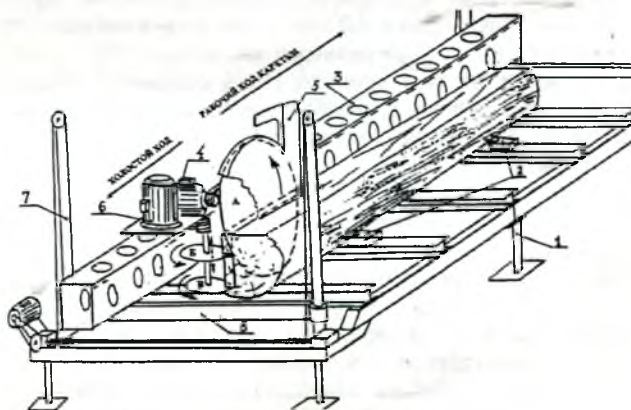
Конструкция круглопильного станка для продольной распиловки бревен:
